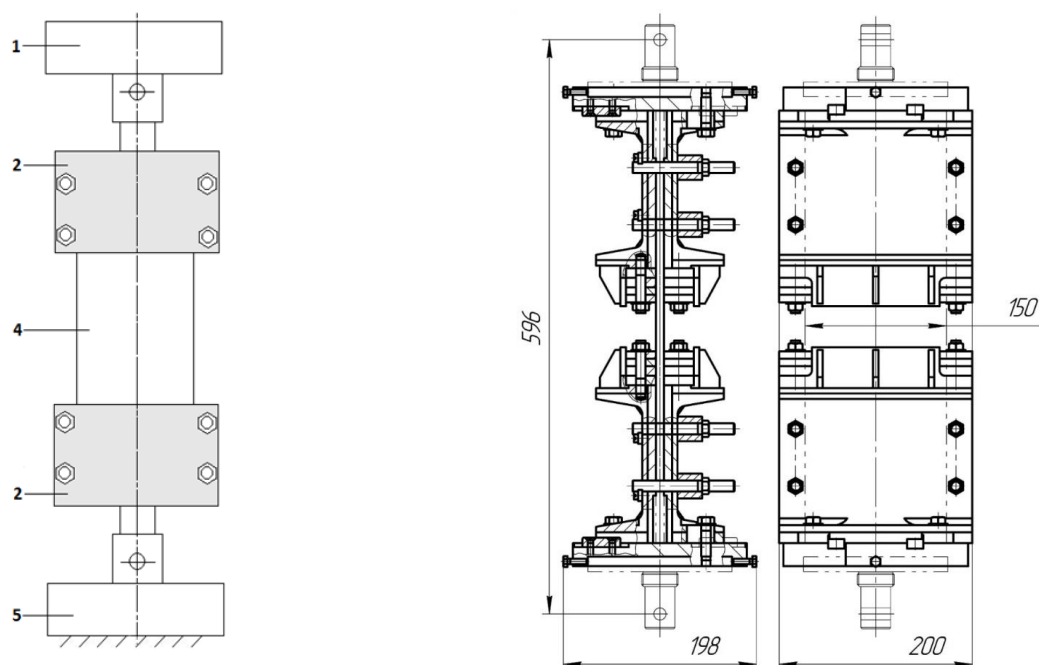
Схема закрепления и эскиз оснастки для проведения испытаний образцов-панелей на сжатие (1 – подвижная траверса; 2 – захваты; 4 – образец; 5 – неподвижная траверса)
